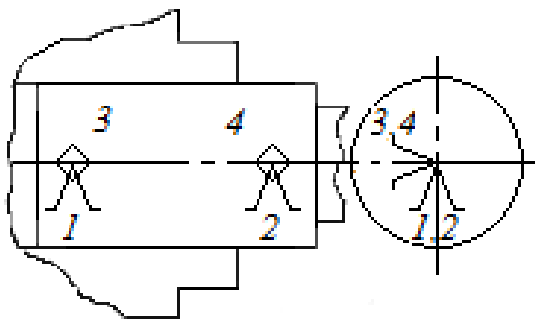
Установка вала при його консольному кріпленні в патроні
